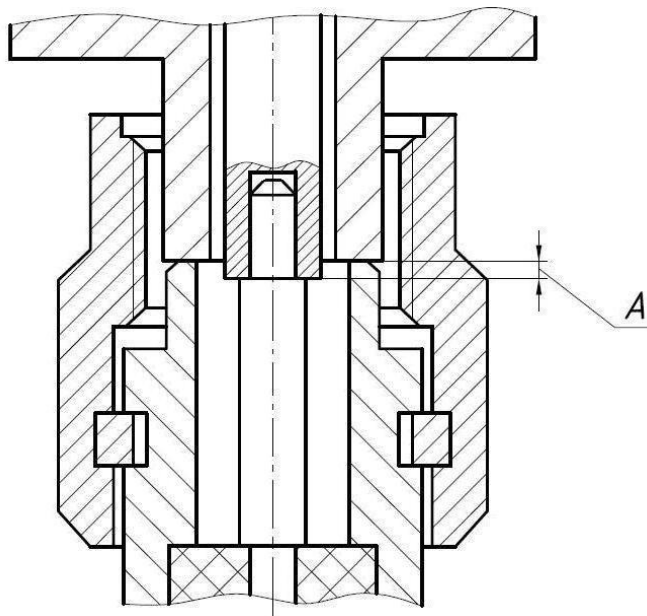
Проверка размера «А» соединителя «вилка»
